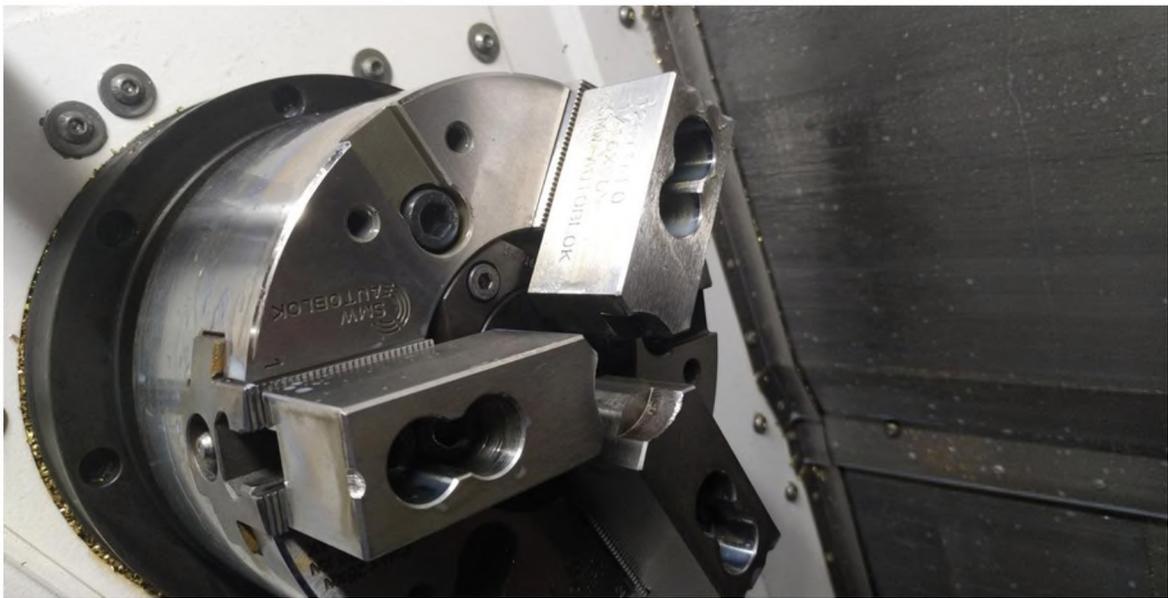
Загальний вигляд трьохкулачкового патрона.
